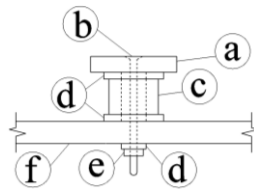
Montaje del anillo de fuerza sobre la viga de acero a) planchuela de acero de 9 mm de espesor b) tornillo de cabeza plana c) anillo de fuerza d) arandelas metálicas e) tuerca metálica f) viga de acero.
